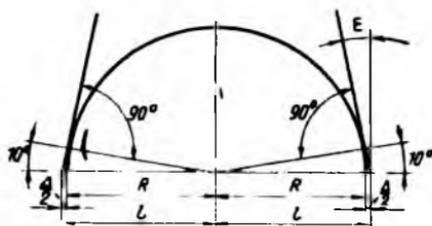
Геометрия профиля штапа, исключающая необходимость кривой боковой обточки зубьев фрезы
